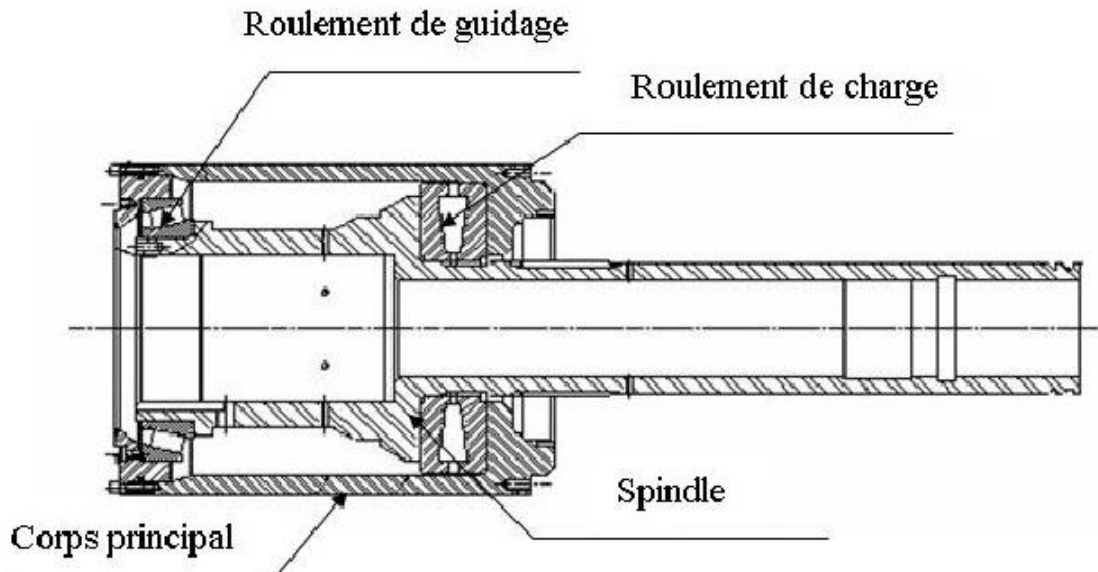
Ensemble (Corps principal et Spindle). [4]
